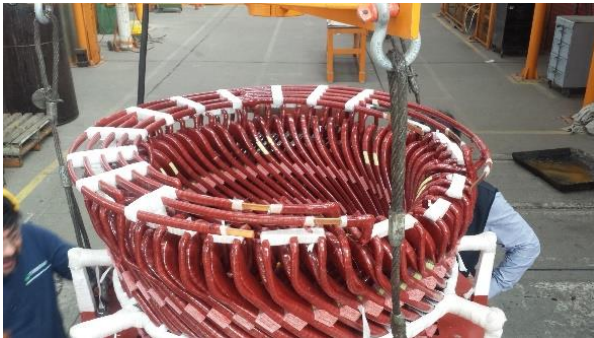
Zona del devanado mostrando el conexionado y cables de salida
